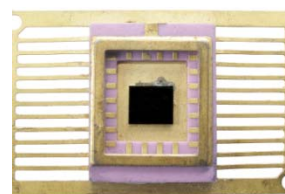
Внешний вид металлокерамического корпуса со смонтированным п/п Si-кристаллом
